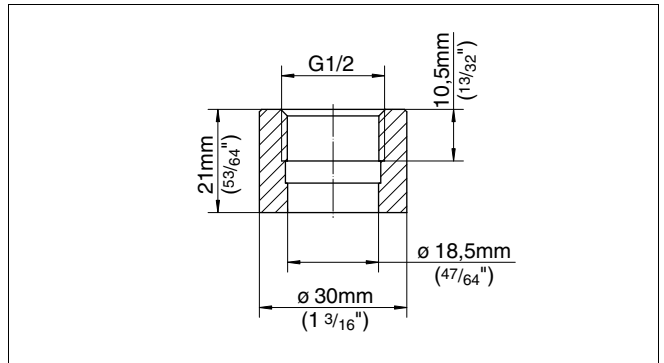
Medidas racor soldado G½ A según ISO 228-1
